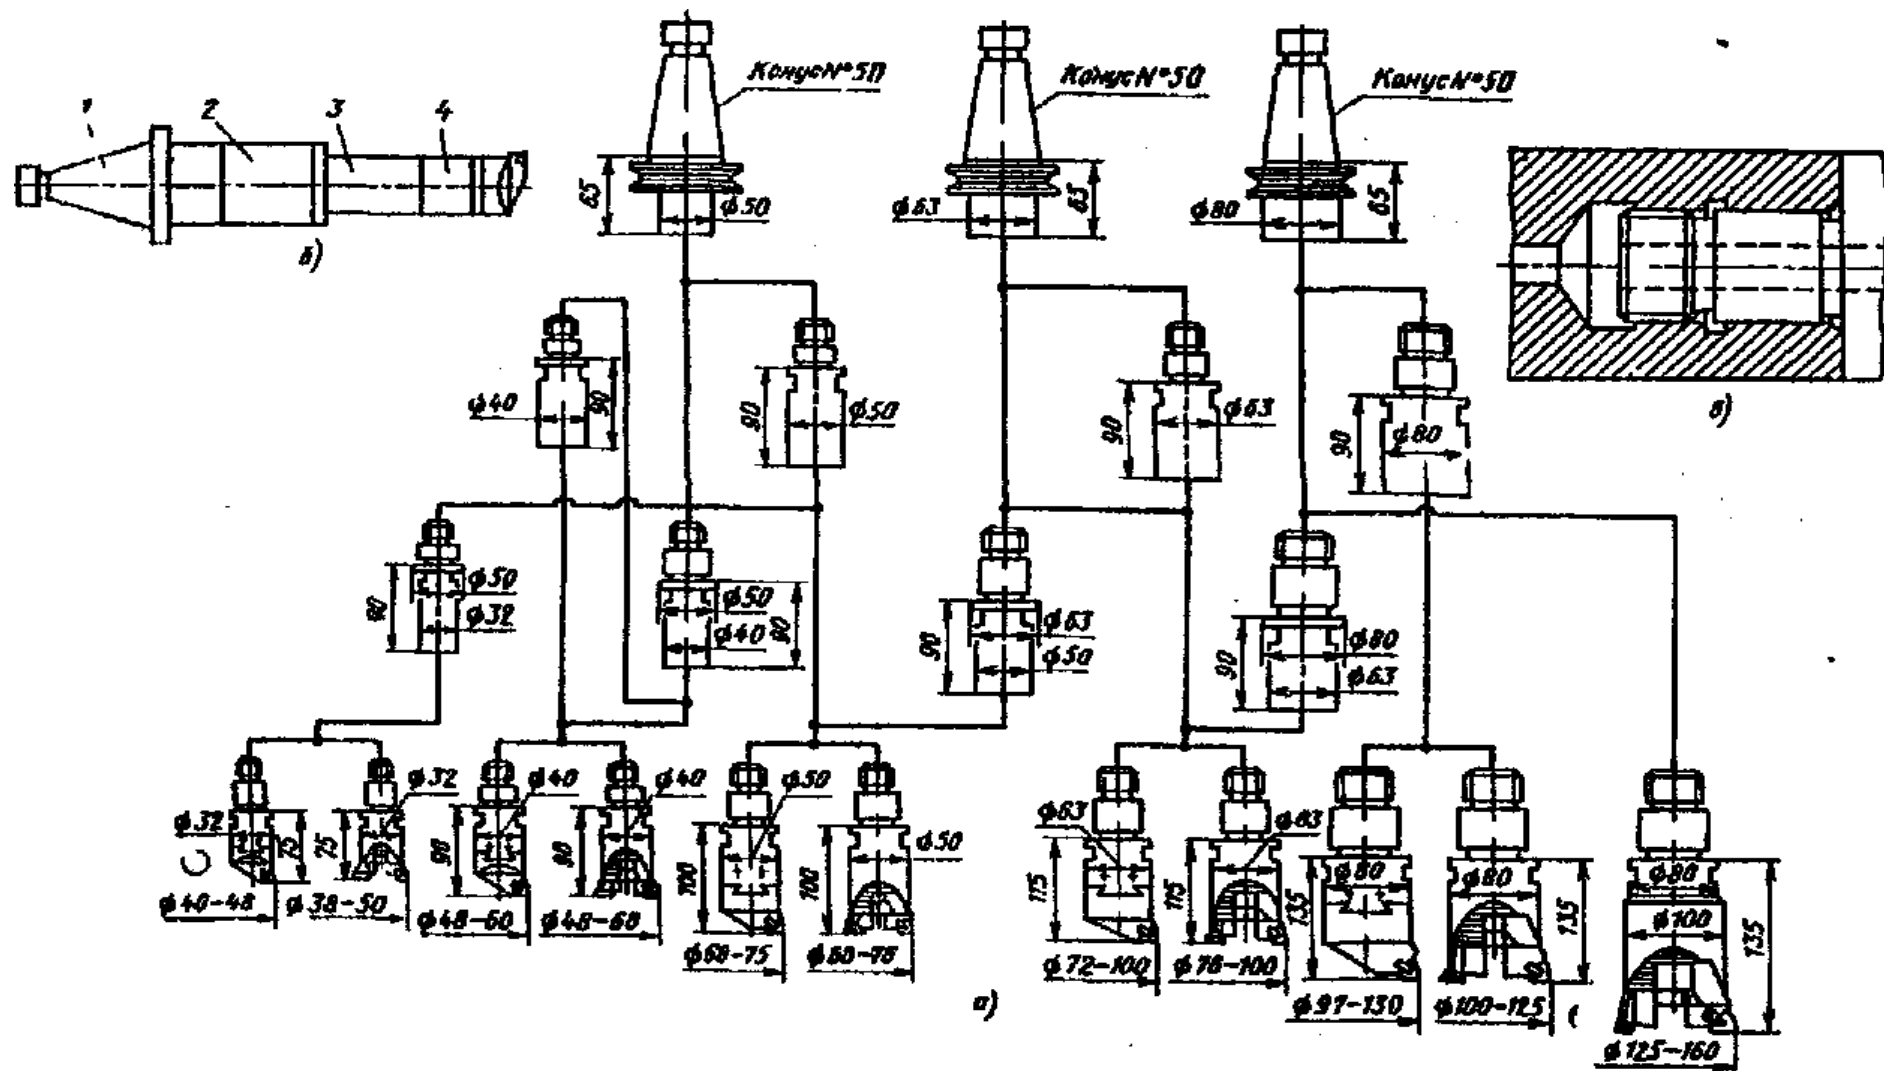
Збірний розточувальний інструмент для багатоцільових верстатів:
